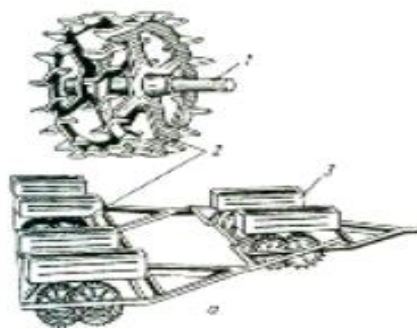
Вид кольчато-шпорового катка ЗКШ-6
